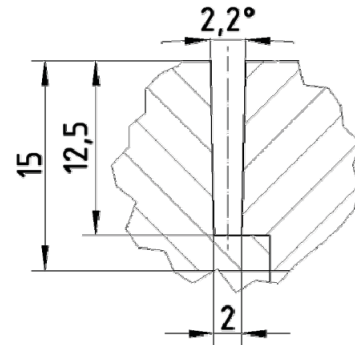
Fugenvorbereitung der Schweißproben
